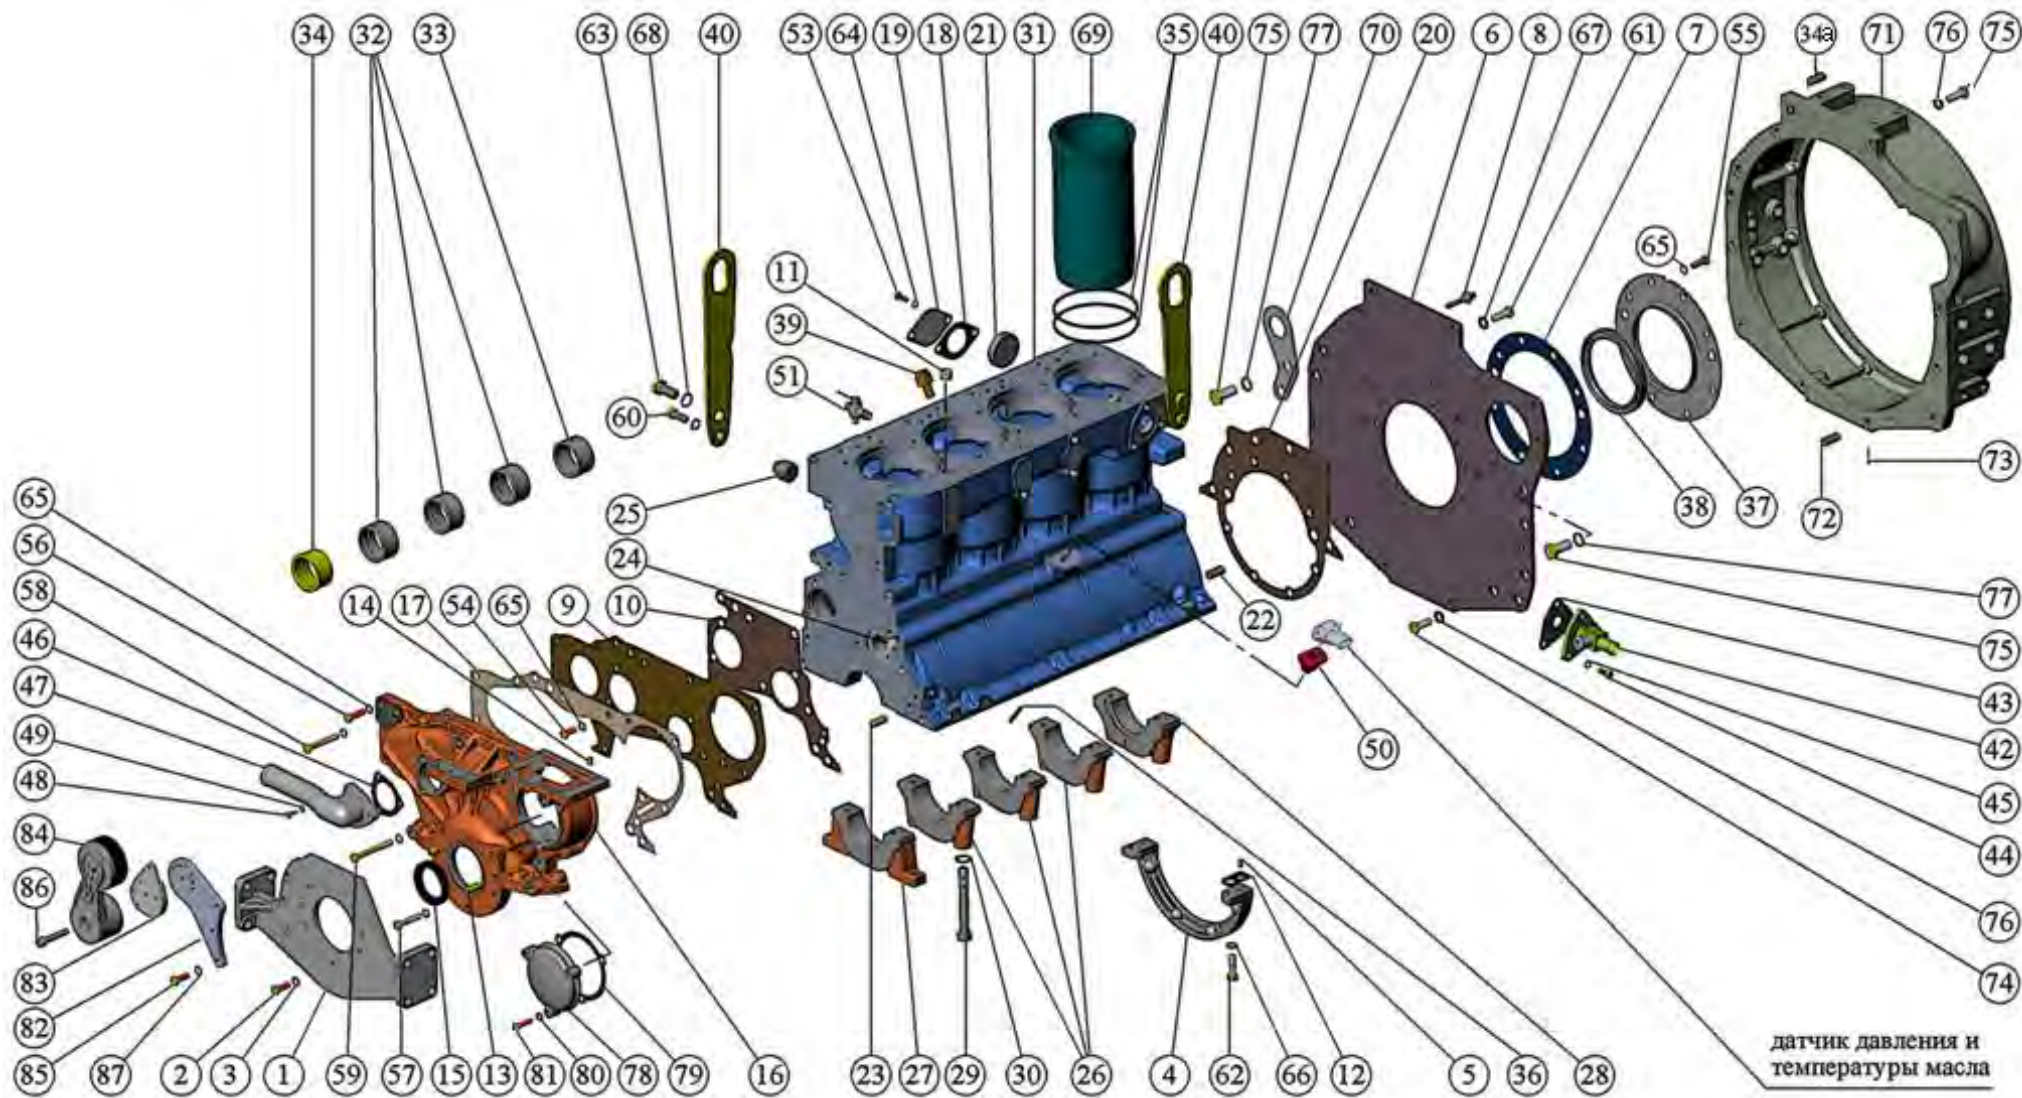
Блок цилиндров. Установка передней опоры. Установка механизма натяжения ремня.
